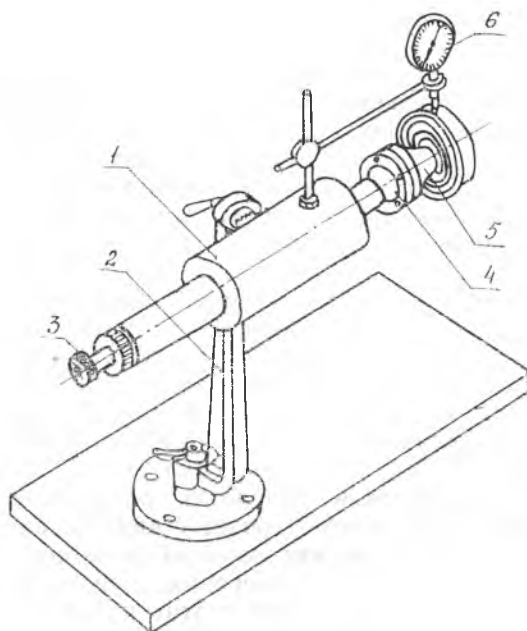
Схема приспособления для проведения лабораторного эксперимента
